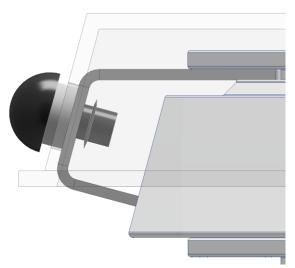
WiNa Stairvent nadat alle pluggen zijn aangebracht
